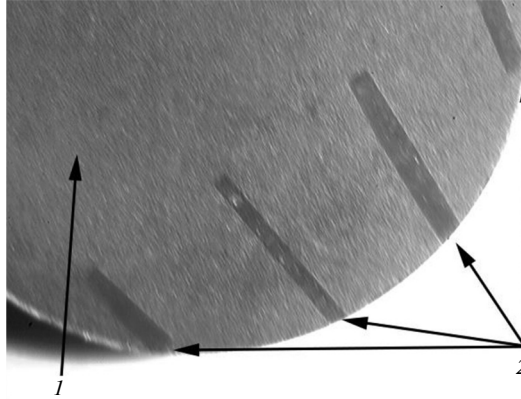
Гибридная алмазно-твердосплавная пластина; 1—алмазный поликристаллический слой; 2—CVD алмаз.
